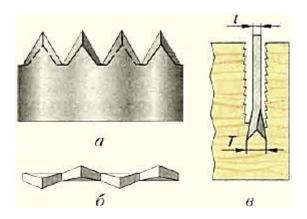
Зубья пилы для поперечного пиления: а — форма зубьев; б — вид разведённых зубьев; в — процесс пиления (вид со стороны пласти заготовки)
